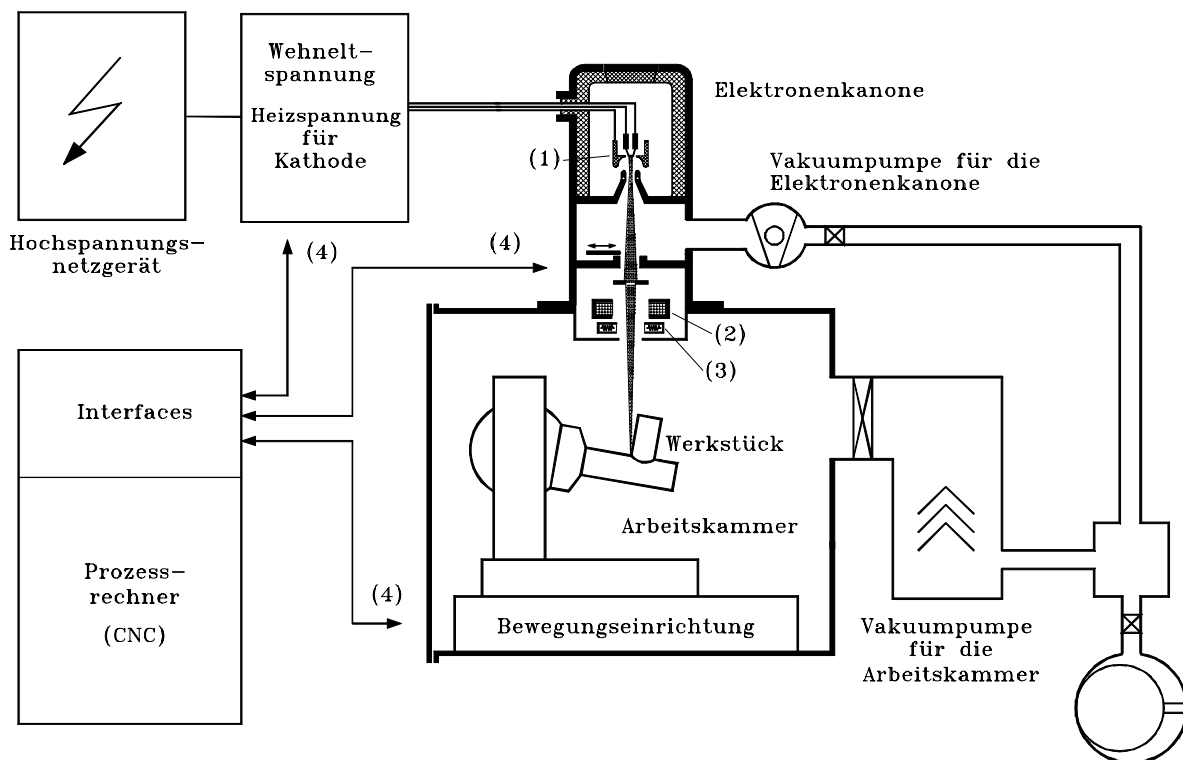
Die typischen Komponenten einer Elektronenstrahl-Schweißanlage:
